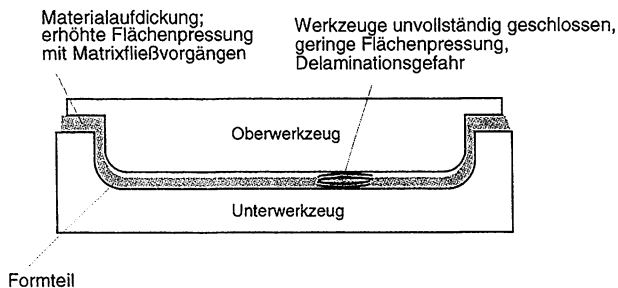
Druckzustände im geschlossenen Formwerkzeug (Querschnitt durch den Werkzeug-Eckenbereich)
